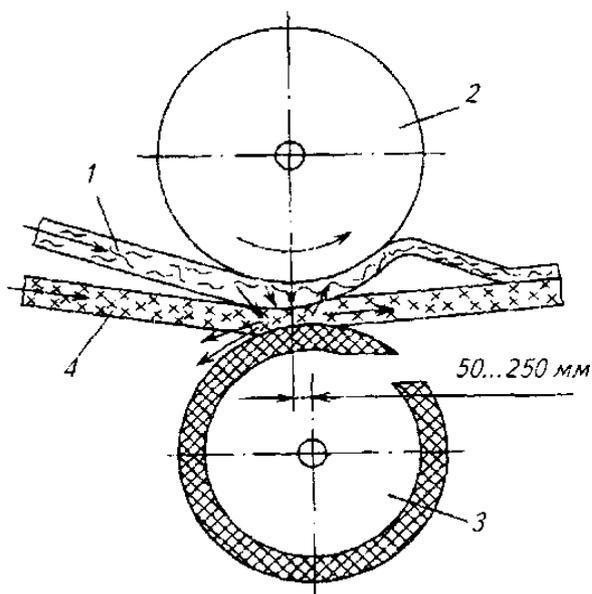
Схема расположения валов обычного двухвального пресса:
